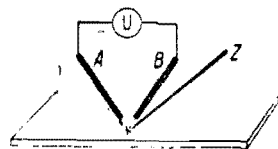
Сварка с дополнительной сварочной проволокой и с отдельными электродами для дуги А и В.
